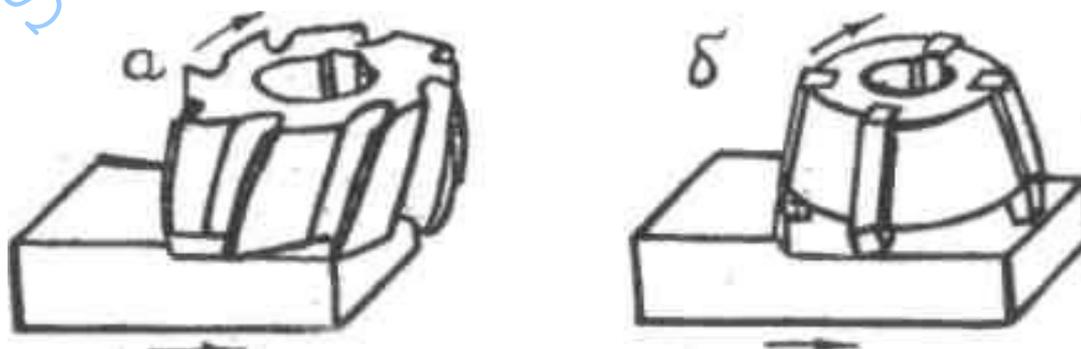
Схема фрезерования концевыми фрезами
